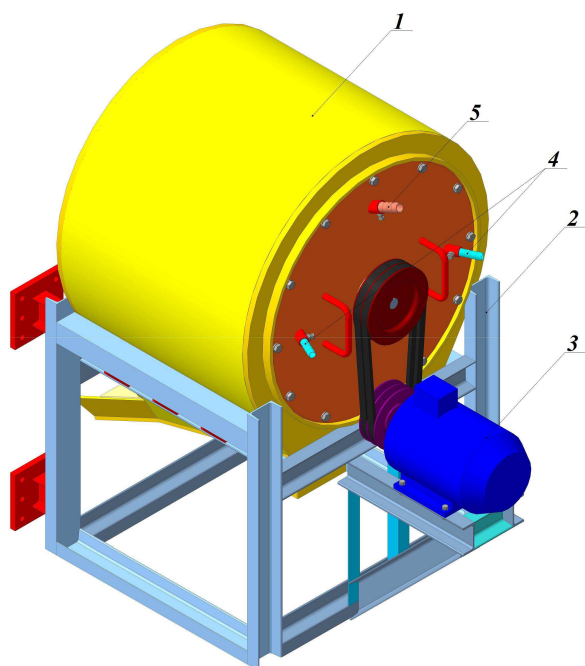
Общий вид головного модуля центробежного сепаратора с непрерывной разгрузкой СЦ-600ГН:
